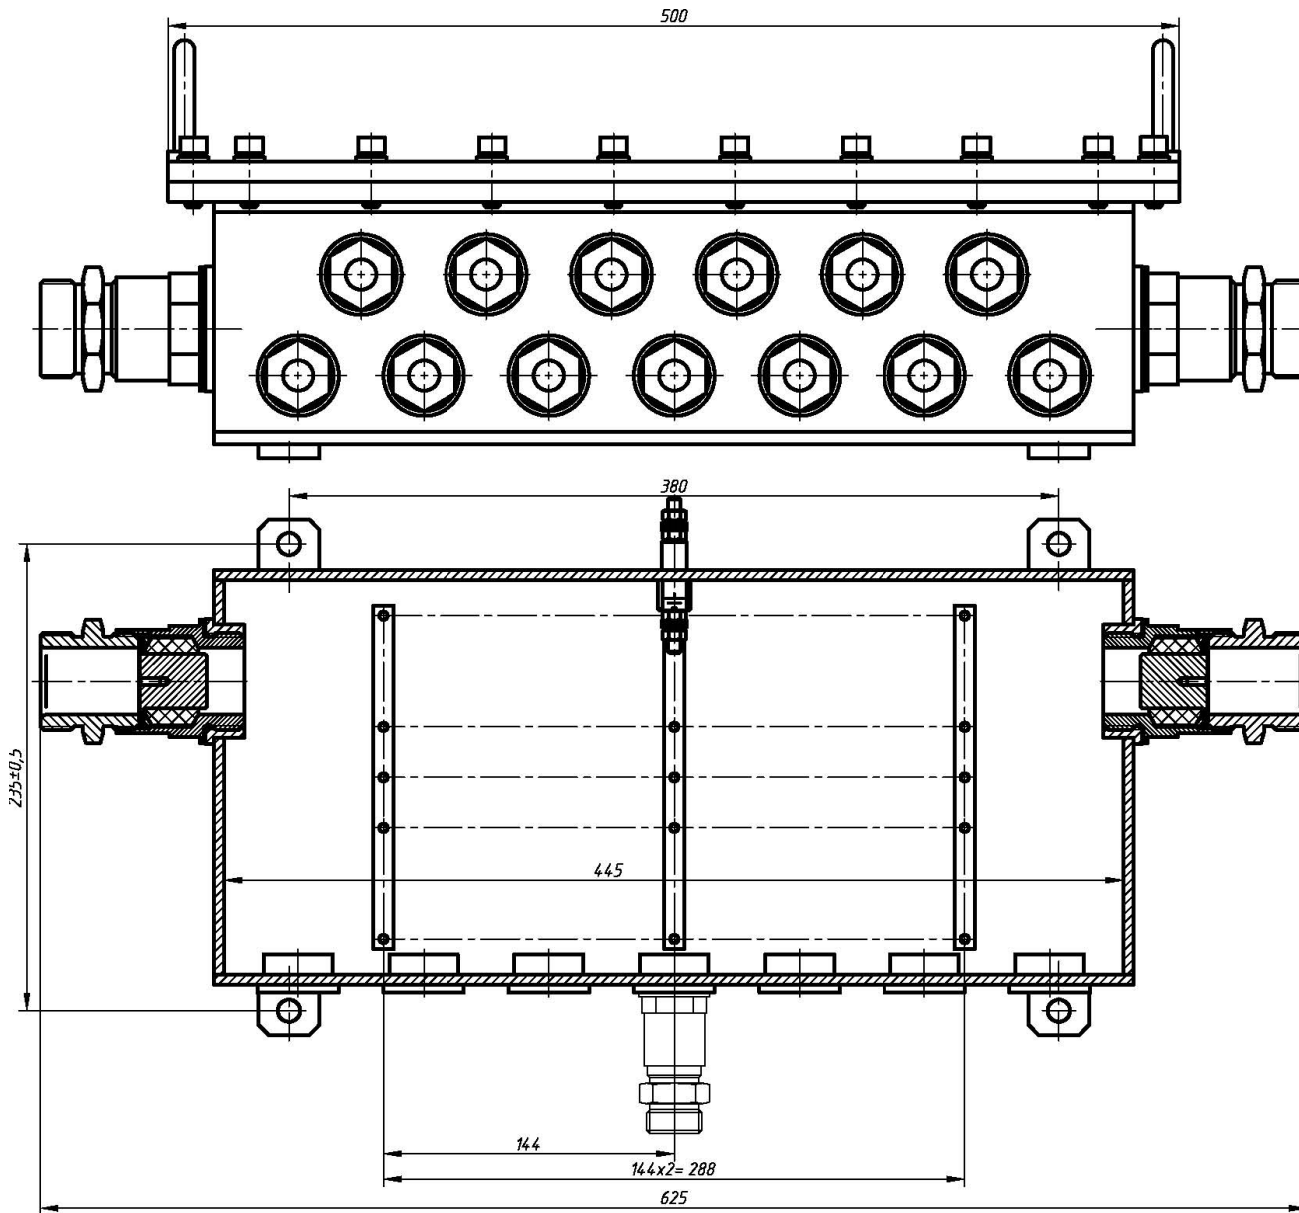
Габаритный чертеж коробки EhКСУВ-ПС500.
